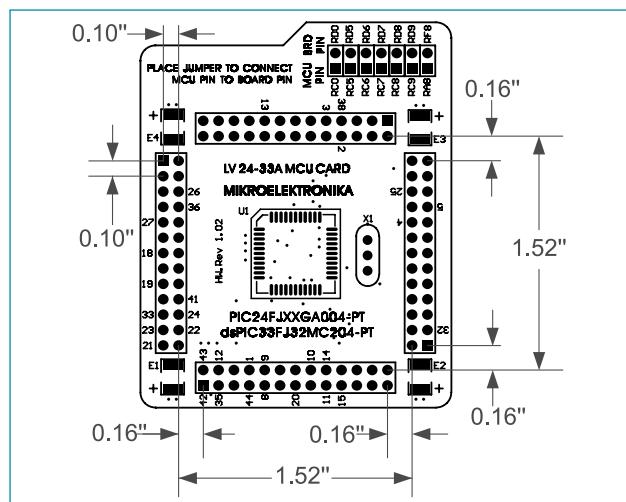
Dimensiones de la tarjeta MCU para la MCU Card 12
